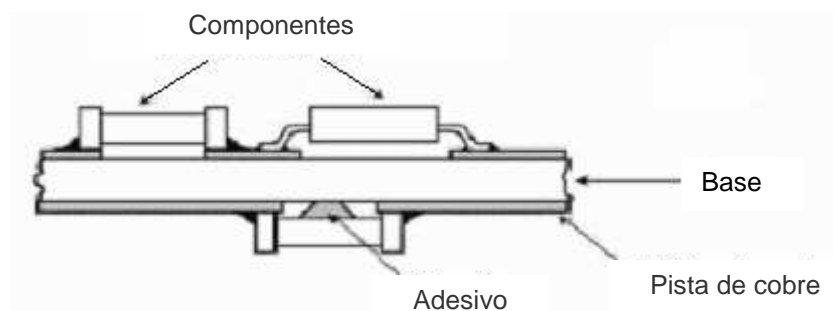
“Surface-Mounted Technology” aplicada à montagem de componentes na placa [28].
